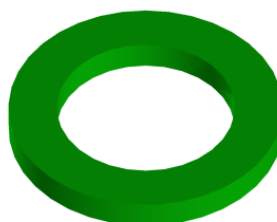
Výstupní materiál s tloušťkou 3 mm
